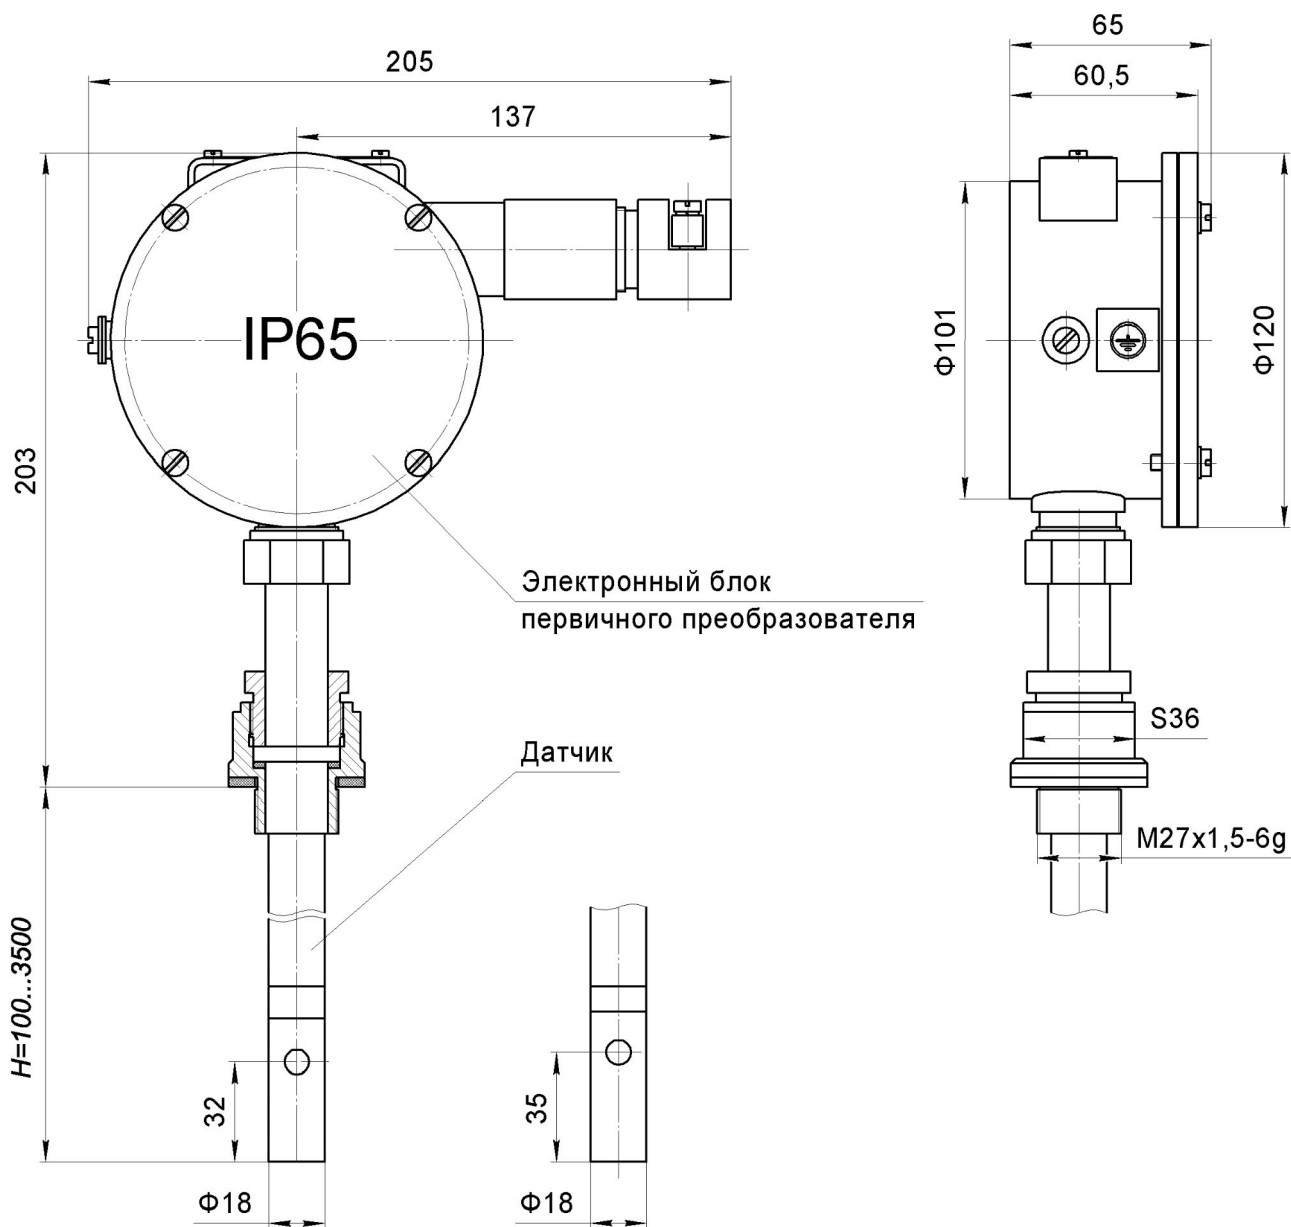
Габаритные, установочные и присоединительные размеры моноблочного первичного преобразователя анализатора АЖК-3101М.1(2; К).АС.Н.100...2000 погружного типа
